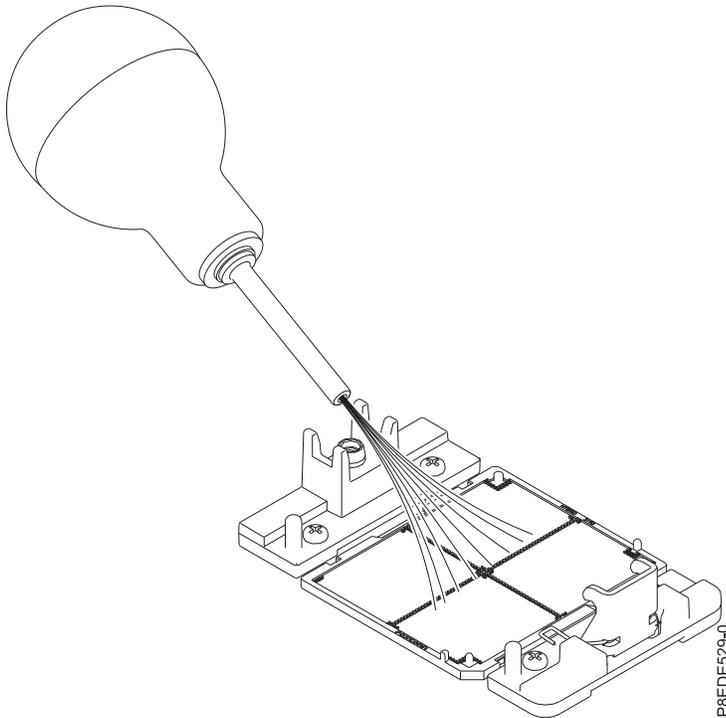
Staub und Fremdkörper vom Systemprozessorsocket entfernen
